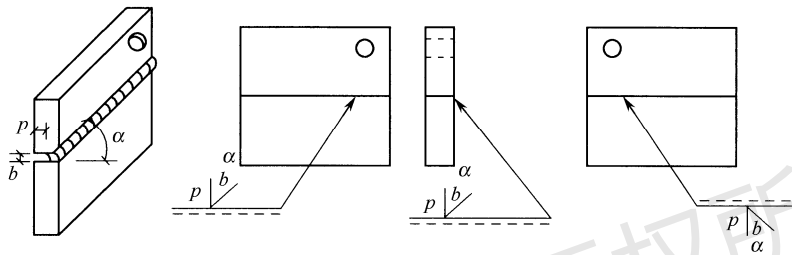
单个焊件带坡口焊缝的标注方法
